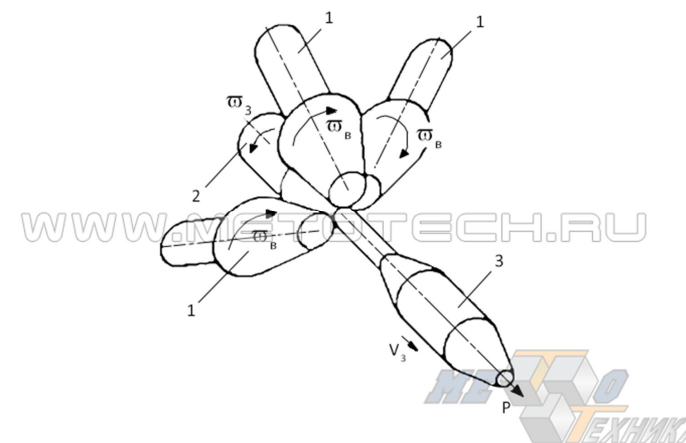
Схема трехвалковой ПВП: 1 – валковый механизм; 2 – тело заготовки; 3 – финишное изделие
